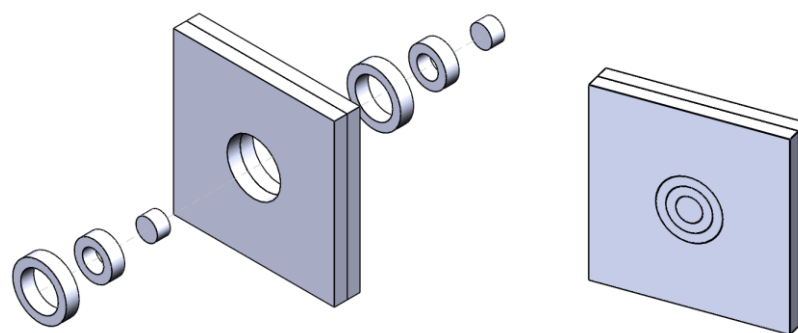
Разделение точечного сварного соединения на зоны
